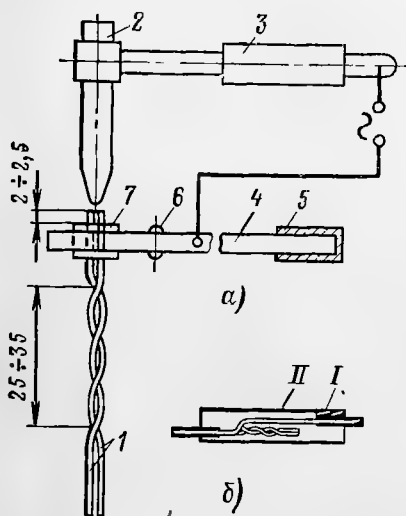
Сварка и изолировка соединений проводов.
